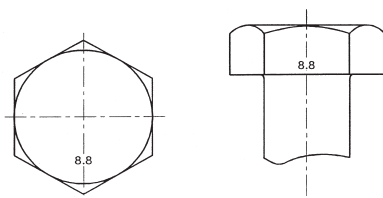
Abb. G: Beispiel für die Kennzeichnung von Sechskantschrauben
